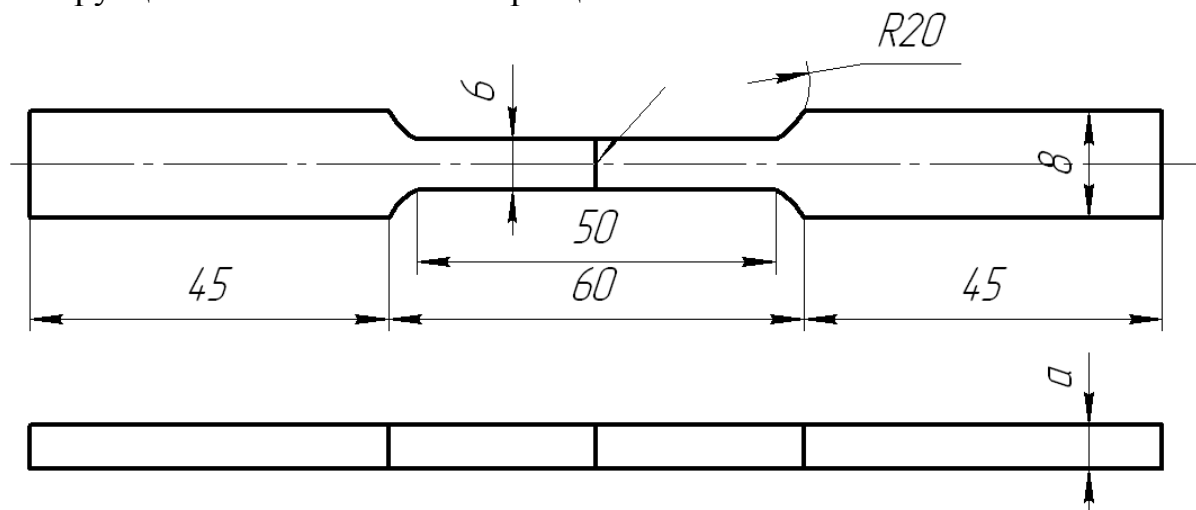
Образец для испытания на сопротивление ударному разрыву
